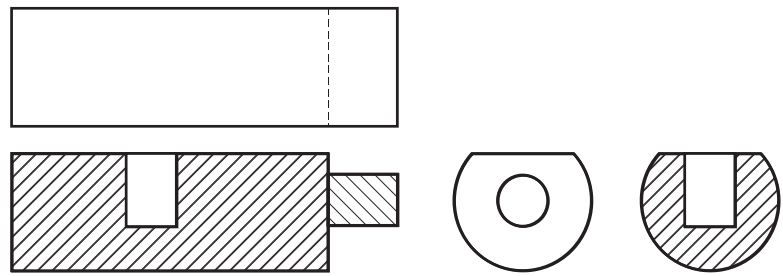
Внешний вид заготовки и изготавливаемого из нее двухступенчатого вала. Здесь пунктиром показано условное разделение цилиндрической поверхности заготовки (круглого проката) на две поверхности, обрабатываемые в соответствии с отдельными технологическими операциями
